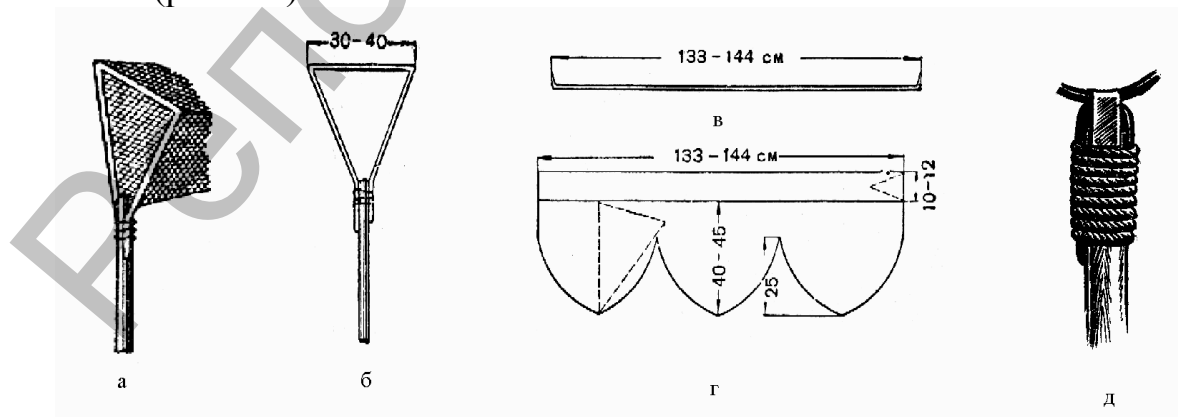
Изготовление водного сачка: а – готовый сачок, б – проволочный каркас на палке, в – приготовление проволоки, г – выкройка мешковины, д – крепление каркаса к палке.
